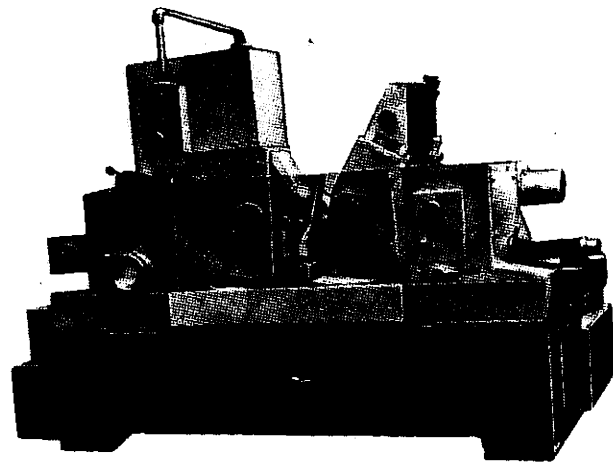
Круглошлифовальный бесцентровый станок ЗМ184
